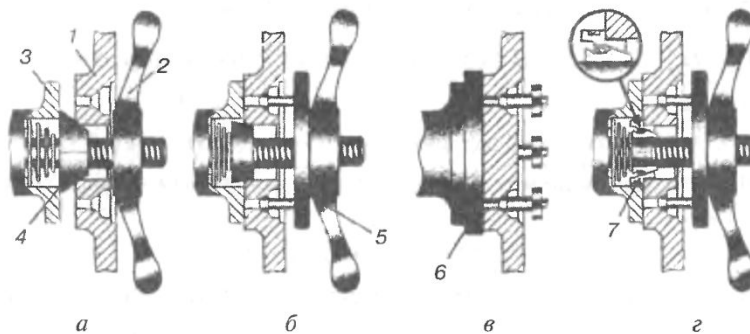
Способы и устройства центрирования колеса на валу балансировочного станка: а — центрирование колеса конусным адаптером по центральному отверстию; б — центрирование колеса по крепежным отверстиям винтовым зажимным устройством; в — центрирование колеса по крепежным отверстиям фланцевым зажимным устройством; г — центрирование колеса по центральному и крепежным отверстиям винтовым зажимным устройством; 1 — колесо; 2 — зажимное устройство; 3 — вал балансировочного станка; 4 — конический адаптер; 5 — фланцевый адаптер; 6 — фланцевый адаптер для колес без центрального отверстия; 7 — цанговый адаптер
